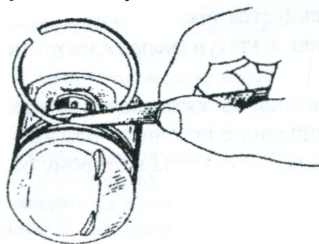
Проверка зазора между поршневыми кольцами и канавкой
